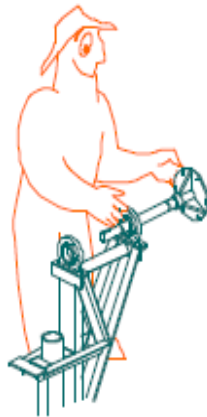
Montaje del Plato Rotor en la Tornamesa.
